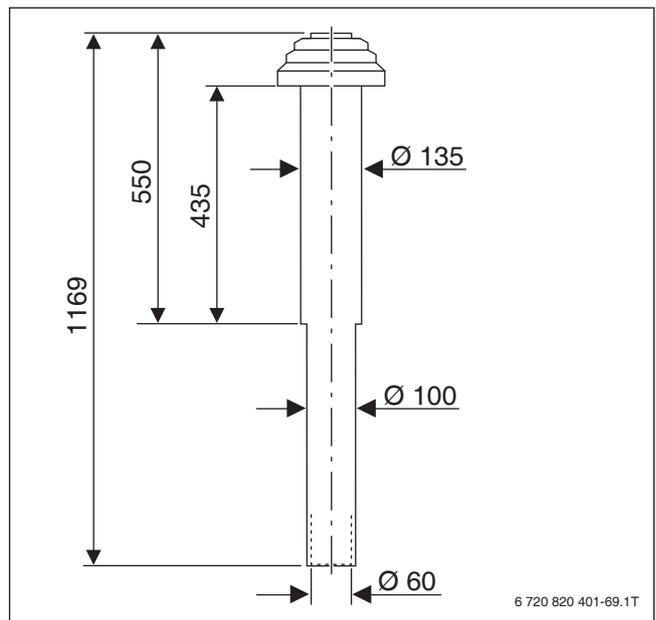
Dachdurchführung Ø 60/100 (Maße in mm)
